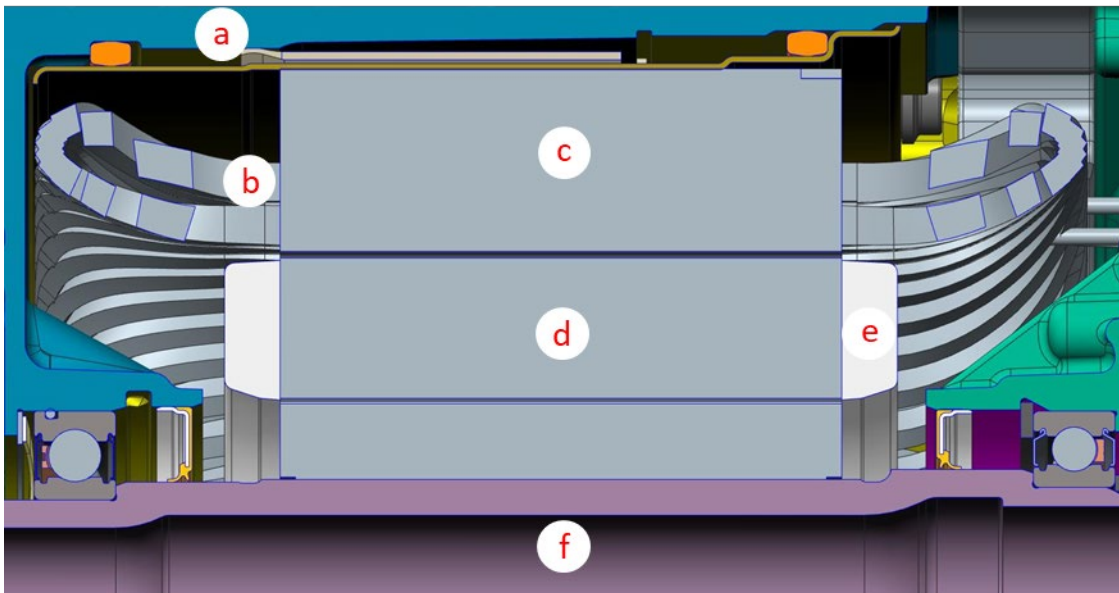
Ausschnitt der E-Maschine mit Kühlmantel
